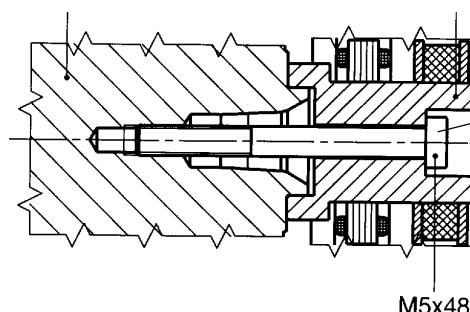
Verbindung Motorwelle - Geberwelle / Joint between motor shaft and encoder shaft
